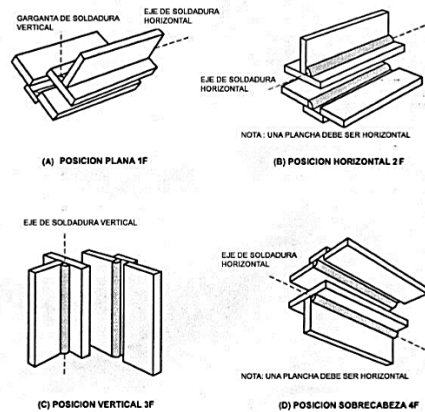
Posiciones para soldadura en filete \*FUENTE: Código para Soldadura Estructural ANSI / AWS
